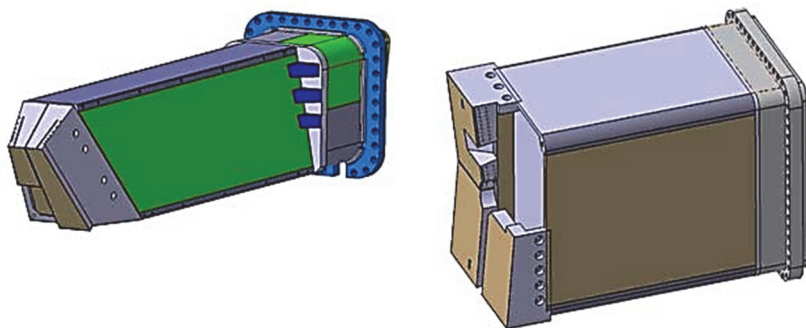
Верхний и экваториальный диагностический порт, установленный на модуле blankets
